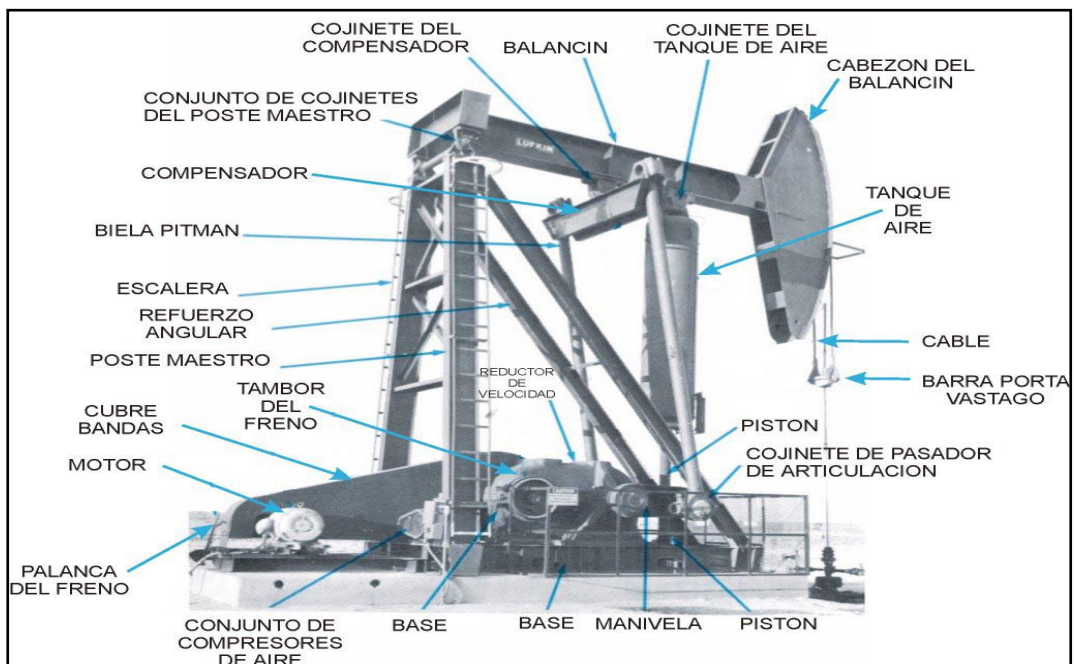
Unidad de Bombeo Mecánico Aerobalanceada.
